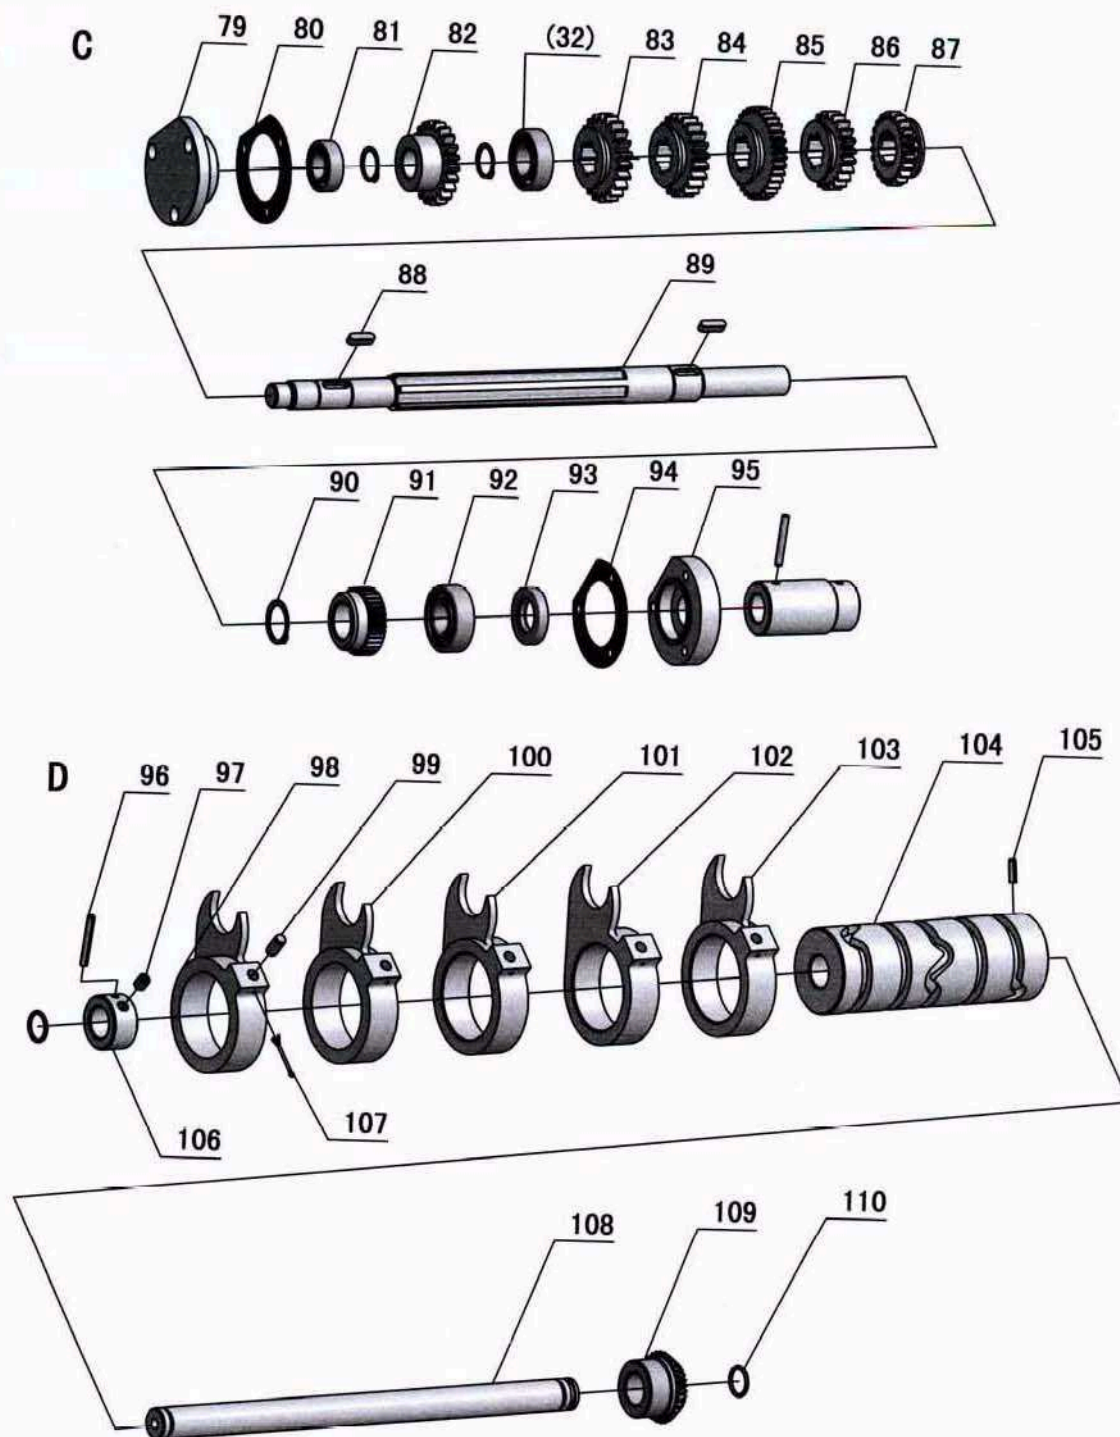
Vorschubgetriebe 3 von 4 - Headstock feed gear 3 of 4
